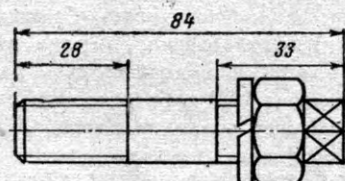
Шпилька М16 для соединения токосъемной коробки редуктора с опорным стаканом
